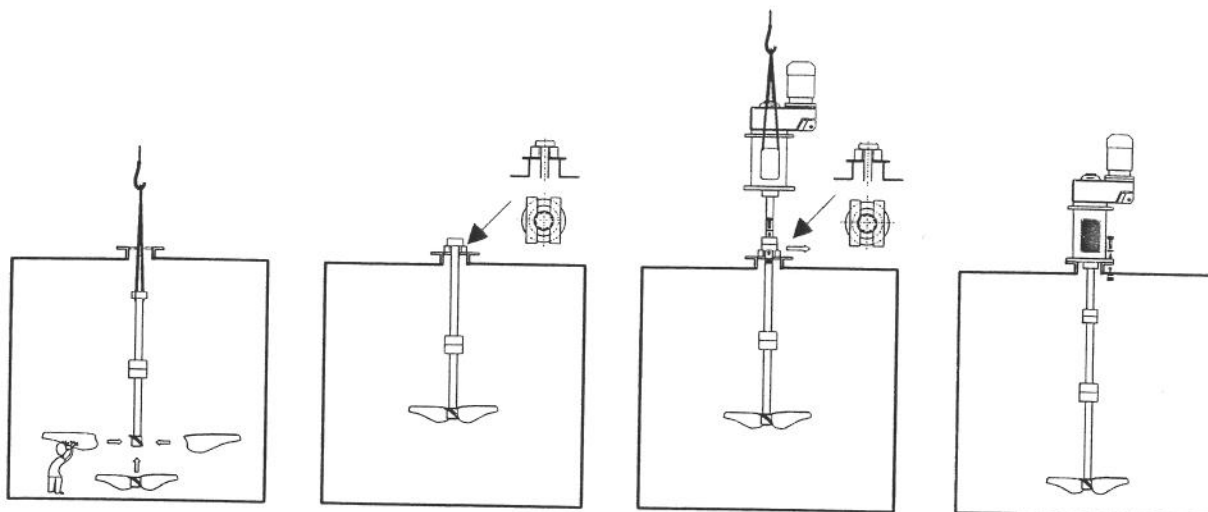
Instalacja mieszadła SCABA z wałem zmontowanym.
